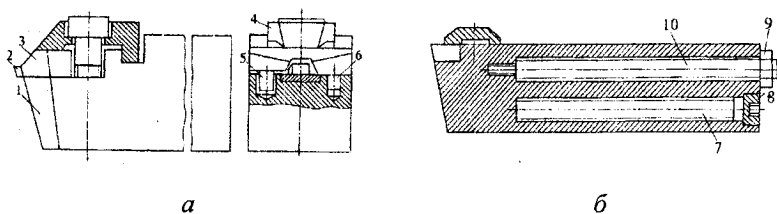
Вібростійкі конструкції інструмента з пружним затиском (а) і з державкою, в якій попередньо створені напруги, протилежні за знаком напругам, що виникають при різанні (б): 1 – державка; 2 – різальний елемент; 3 – сепаратор; 4 – прихват; 5 – рухливий штифт; 6 – штифт; 7 – стискаючий стрижень; 8, 9 – гайка, 10 – розтягуючий стрижень
